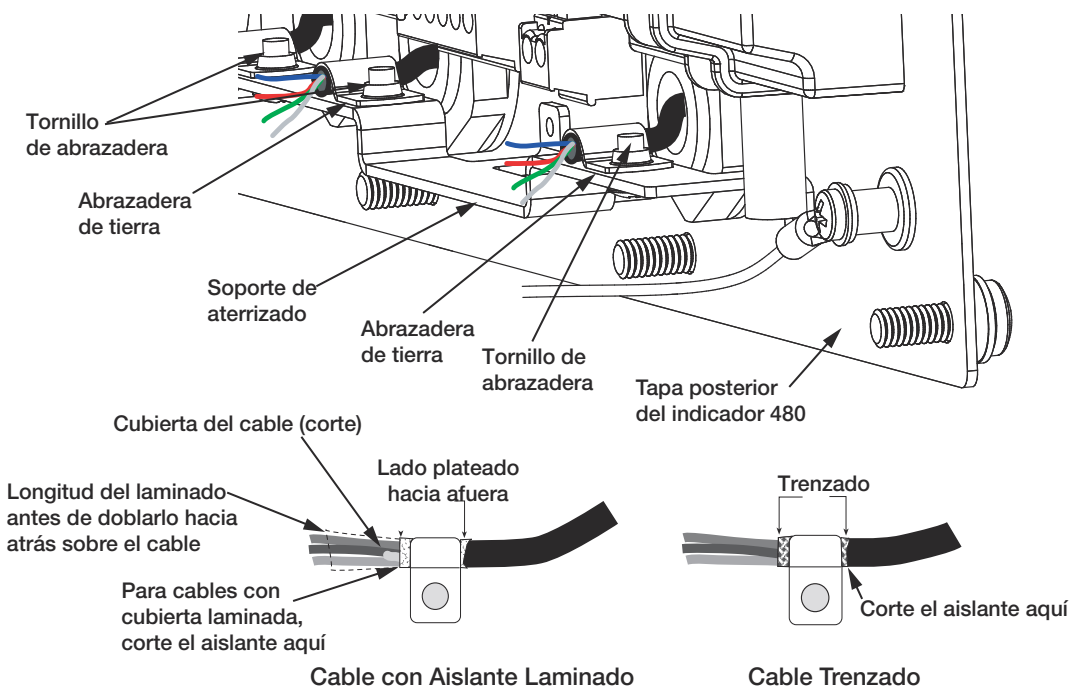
Sujeción de Cables con Cubiertas Laminada y Trenzada, a Abrazaderas de Tierra
